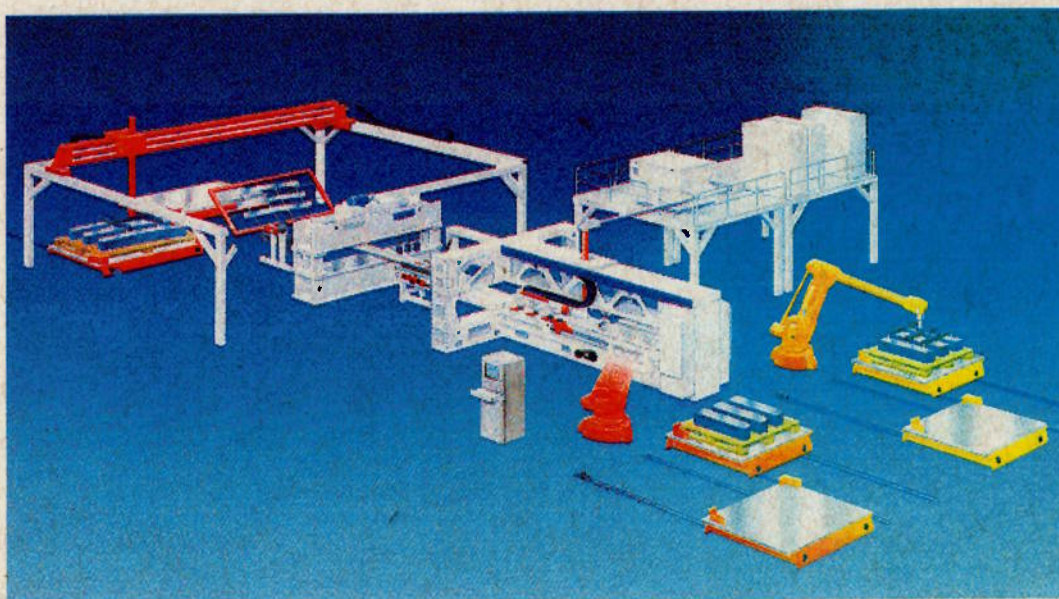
Sistema de Soldagem Soulas – Lay-out do equipamento de solda a laser para fabricação dos blanks soldados [Pincinini99].
